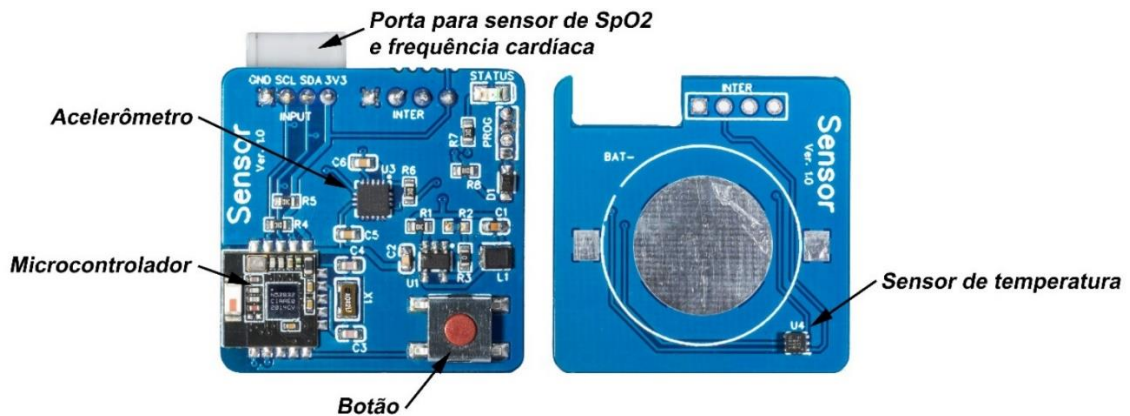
Placas de circuito impresso do coletor e seus principais componentes
